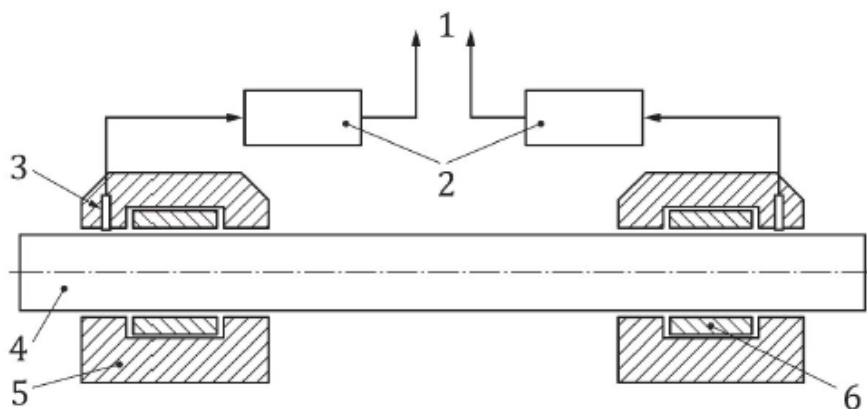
Měřicí body těles ložiskových stojanů [9]
